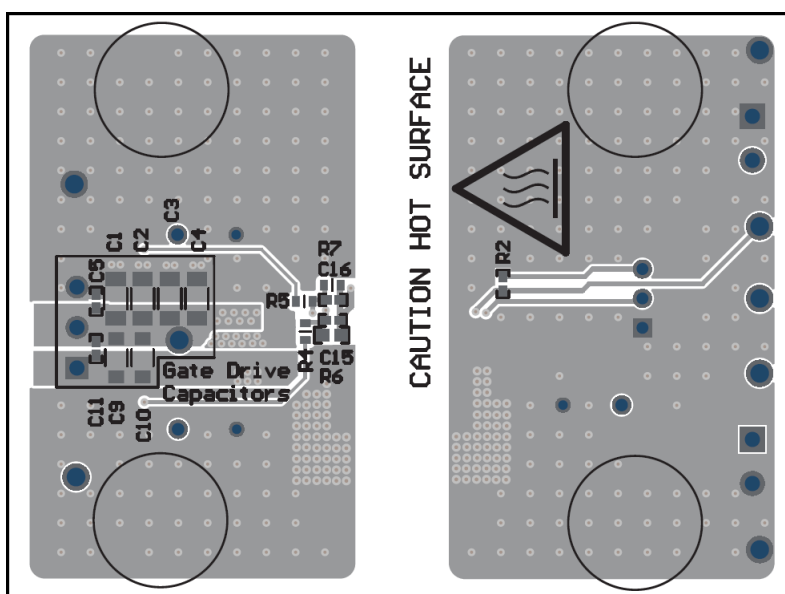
UCC14340-Q1EVM , PCB 底层 , 组装 (镜像视图)
